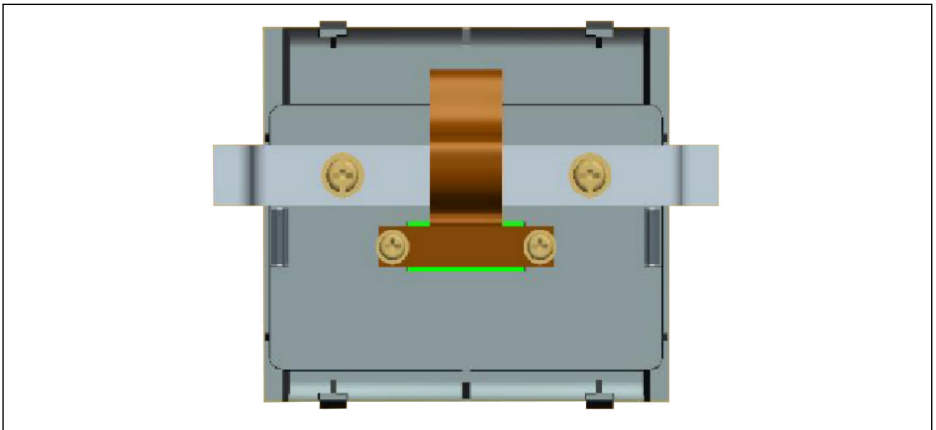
Kabel anschließen und befestigen (Rückansicht)
